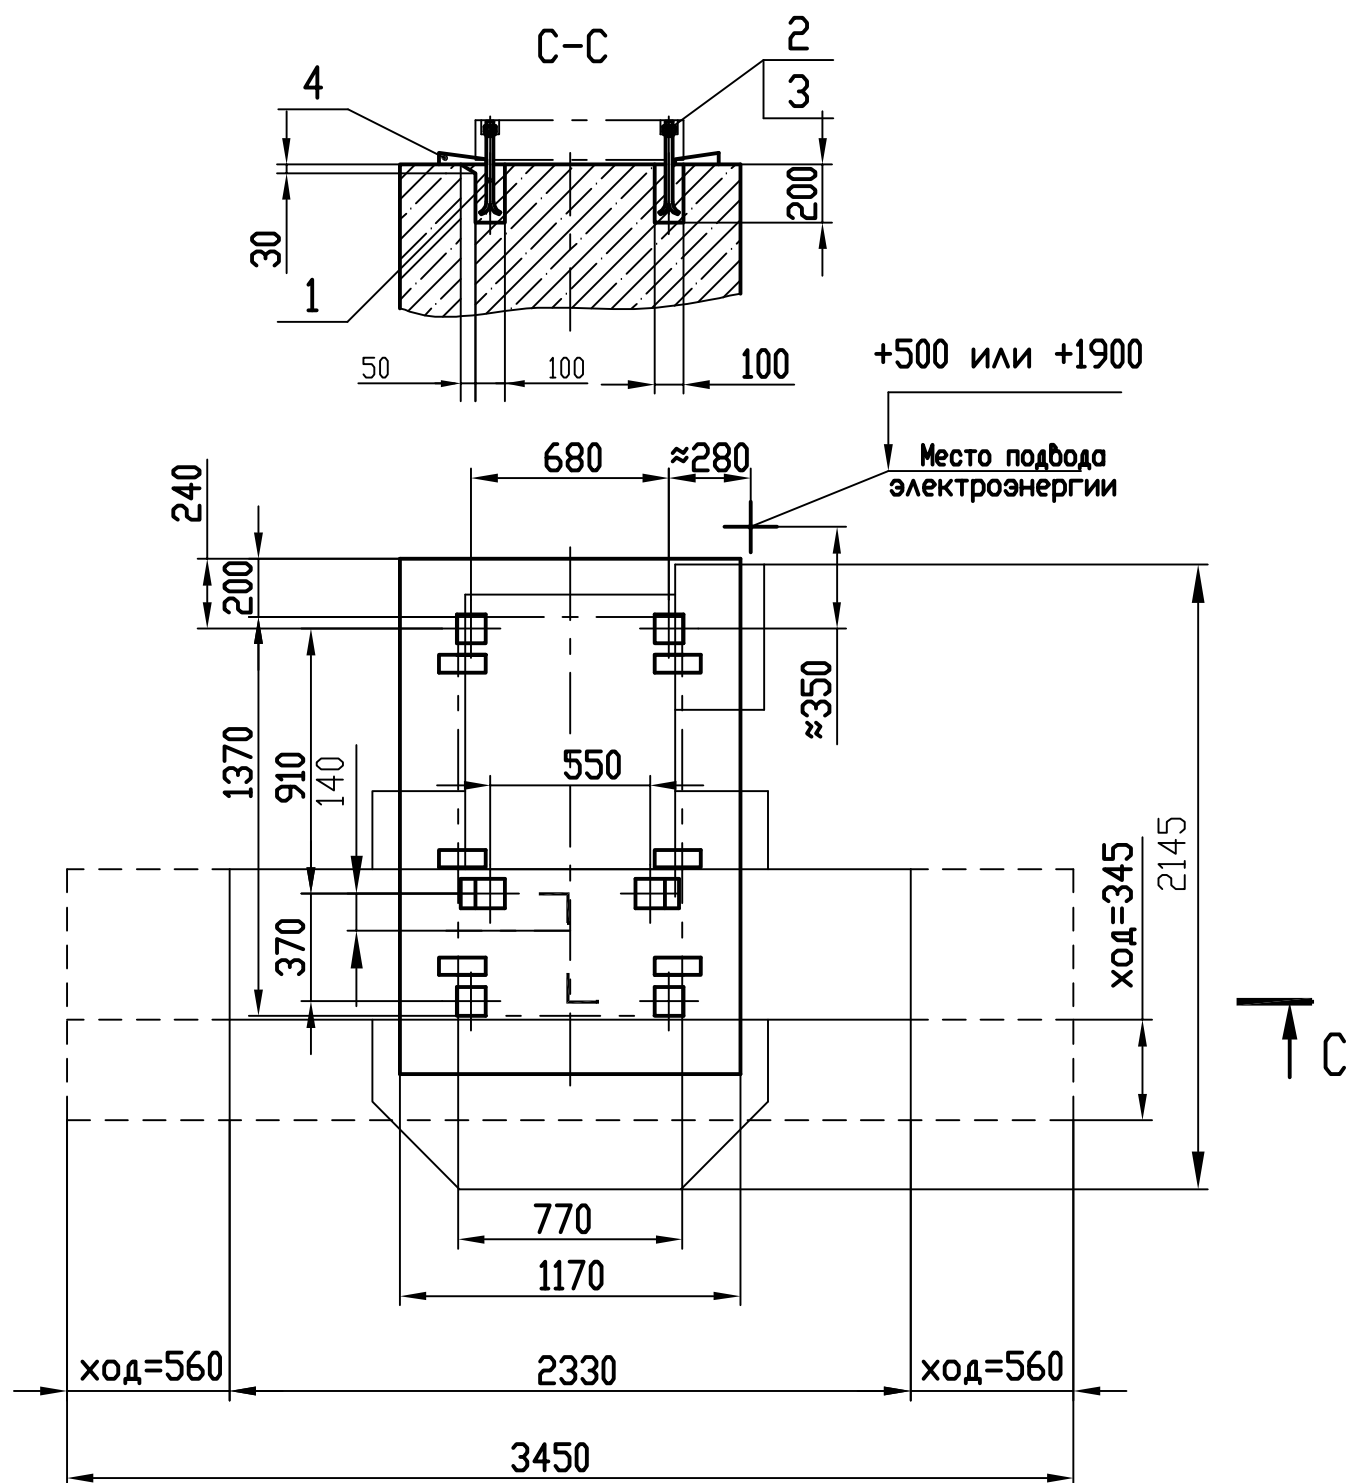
Монтажный чертеж для станков FSS450MRNC, FSS450MRNC-02
